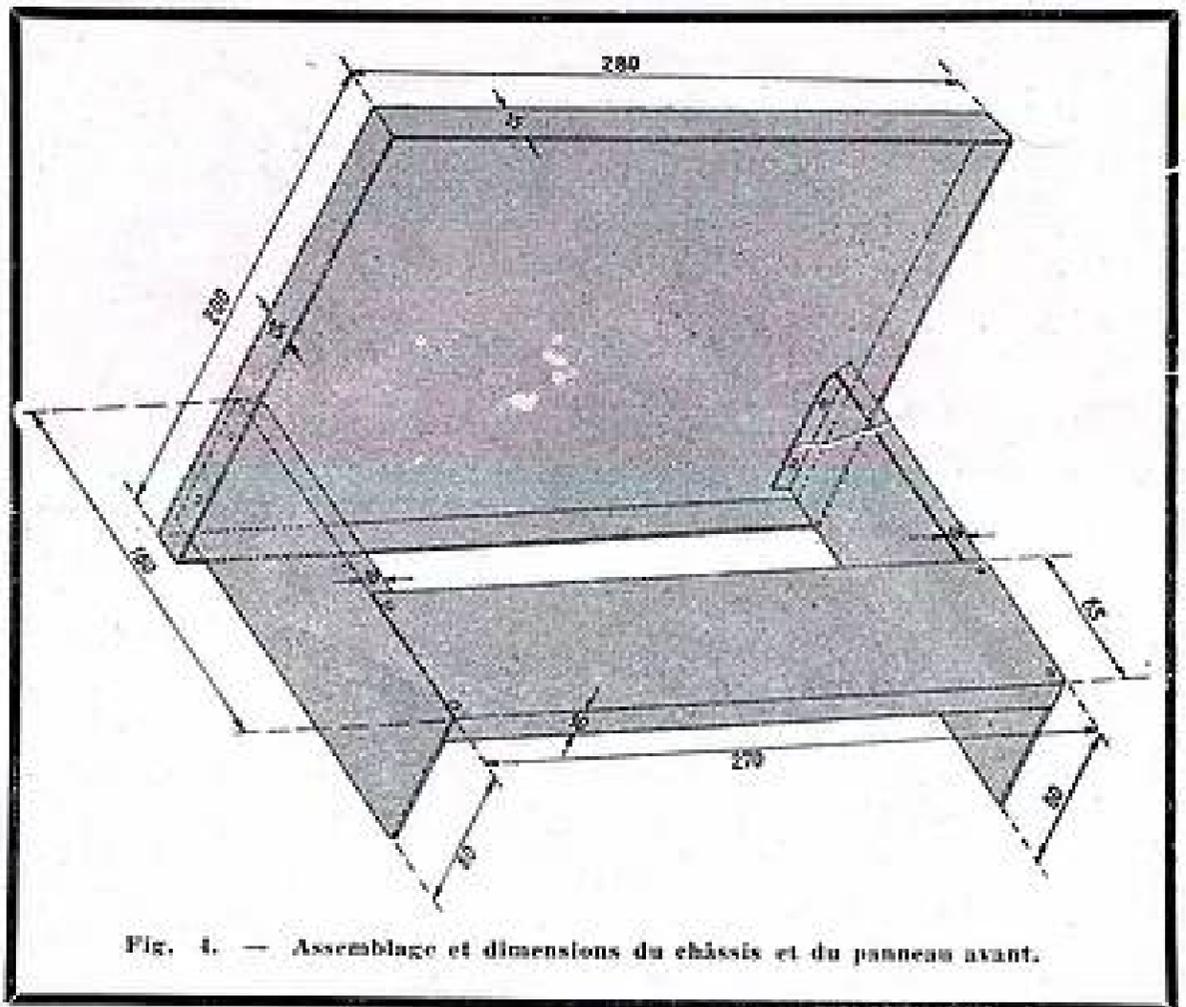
Assemblage et dimensions du châssis et du panneau avant.
